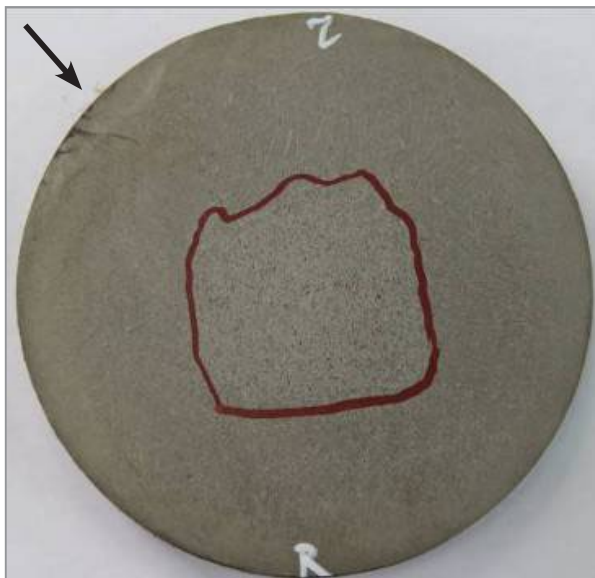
Макроструктура поперечного сечения круглой горячекатаной заготовки диаметром 140 мм стали марки 18Г2АФ
